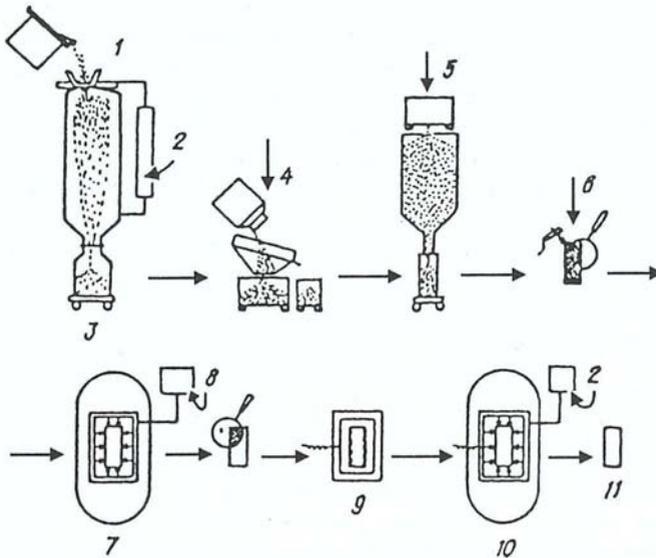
Схема способа «ASEA-Stora»; 1 – заливка расплава; 2 – подача газа; 3 – распыление; 4 – рассев; 5 – заполнение контейнера порошком; 6 – заварка верхней крышки контейнера и контроль герметичности; 7 – ХИП; 8 – контроль герметичности; 9 – предварительный нагрев; 10 – ГИП; 11 – прессование заготовок
